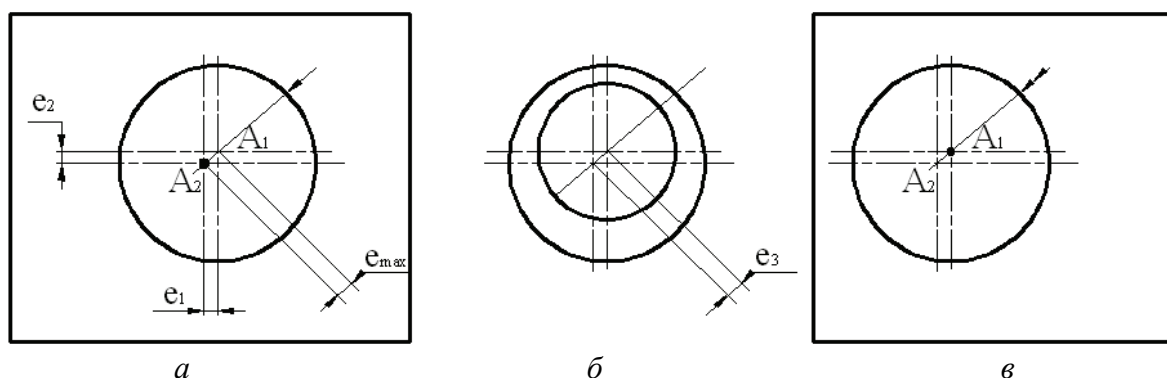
Схемы способов уменьшения радиального биения вала относительно корпуса
